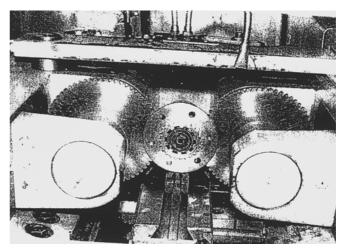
Накатывание боковых поверхностей зуба венца 3-й и 5-й передач кареток синхронизатора коробки передач на профиленакатном станке VPW25 × 100
